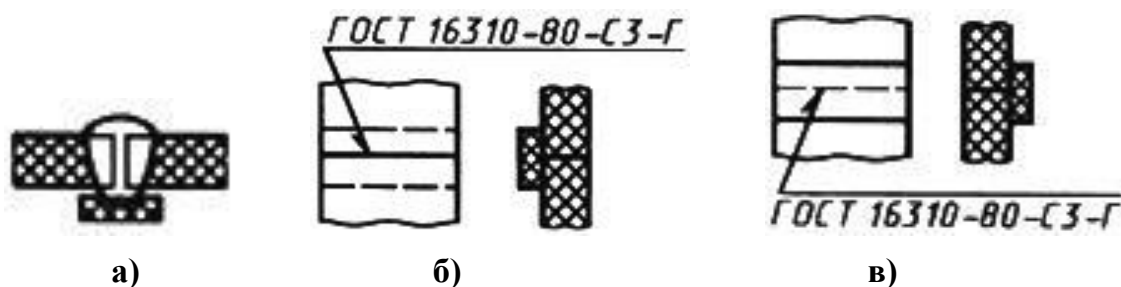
Пример обозначения сварного шва [5]: а – форма поперечного сечения шва; б – обозначение с лицевой стороны; в – обозначение с оборотной стороны
